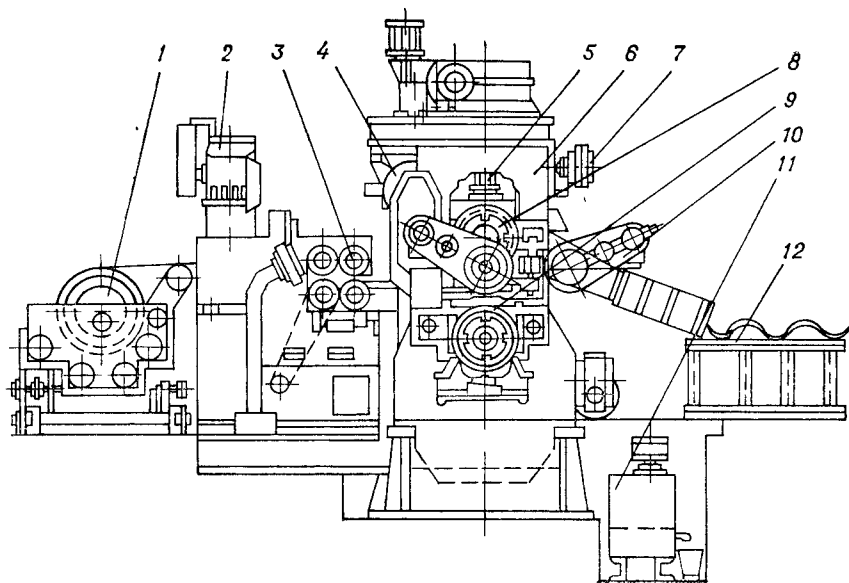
Схема прокатного стана для изготовления спиралей шнеков [22].
